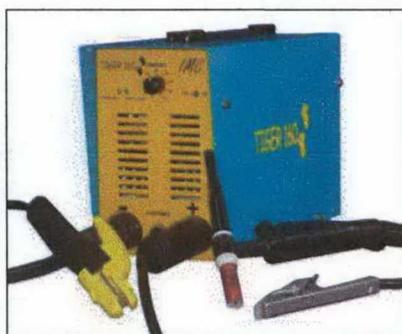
Fonte de Solda TIG modelo TIGER 160
